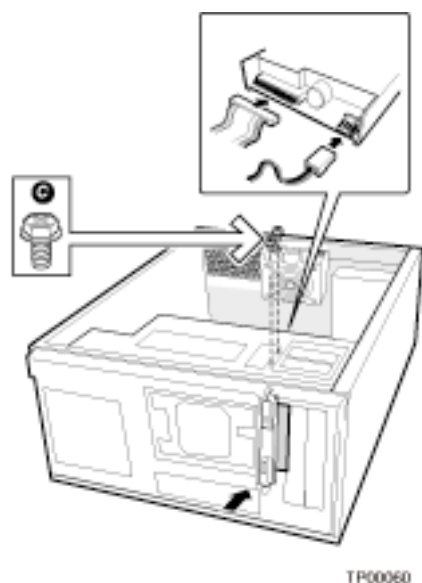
Расположение отсека для жестких дисков для серверного корпуса SC5275-E
